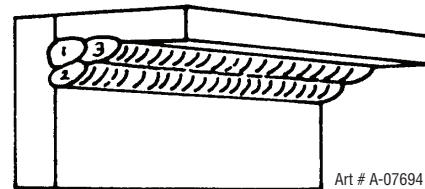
Position au plafond, soudure d'angle
